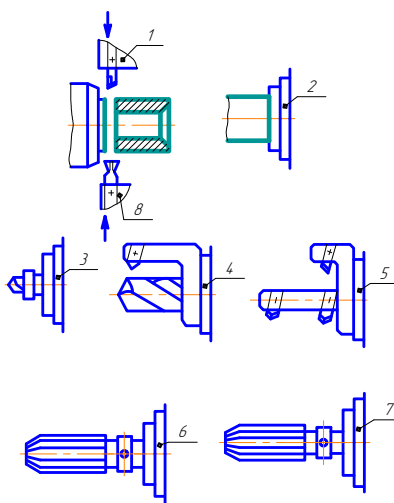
Изготовление втулок из прутка на токарно-револьверном станке: 1) подрезка торца; 2) подача прутка до упора; 3) зацентровка; 4) сверление и обтачивание наружной поверхности; 5) растачивание или зенкерование и обтачивание наружной поверхности со снятием фасок на торце; 6) предварительное развертывание; 7) окончательное развертывание; 8) отрезка.
